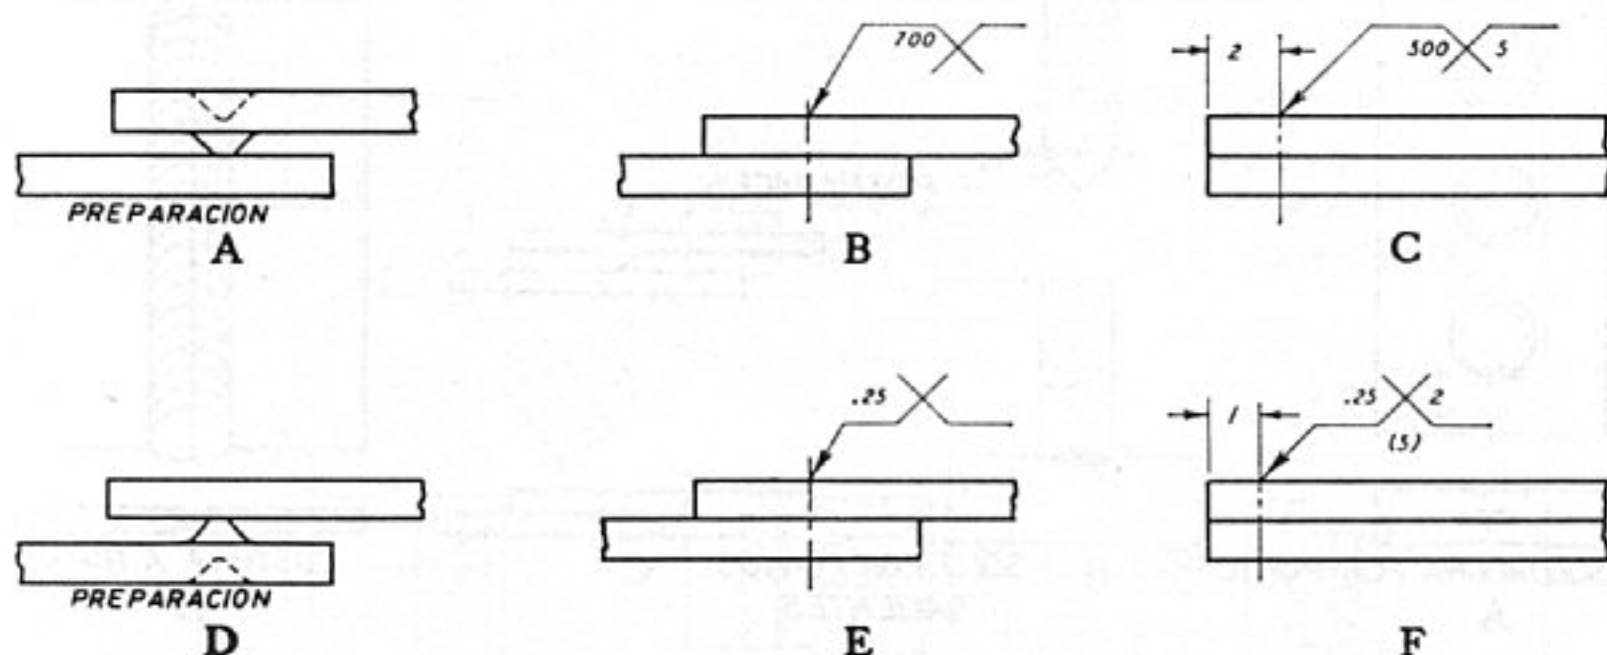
Símbolos de soldadura por puntos salientes.
